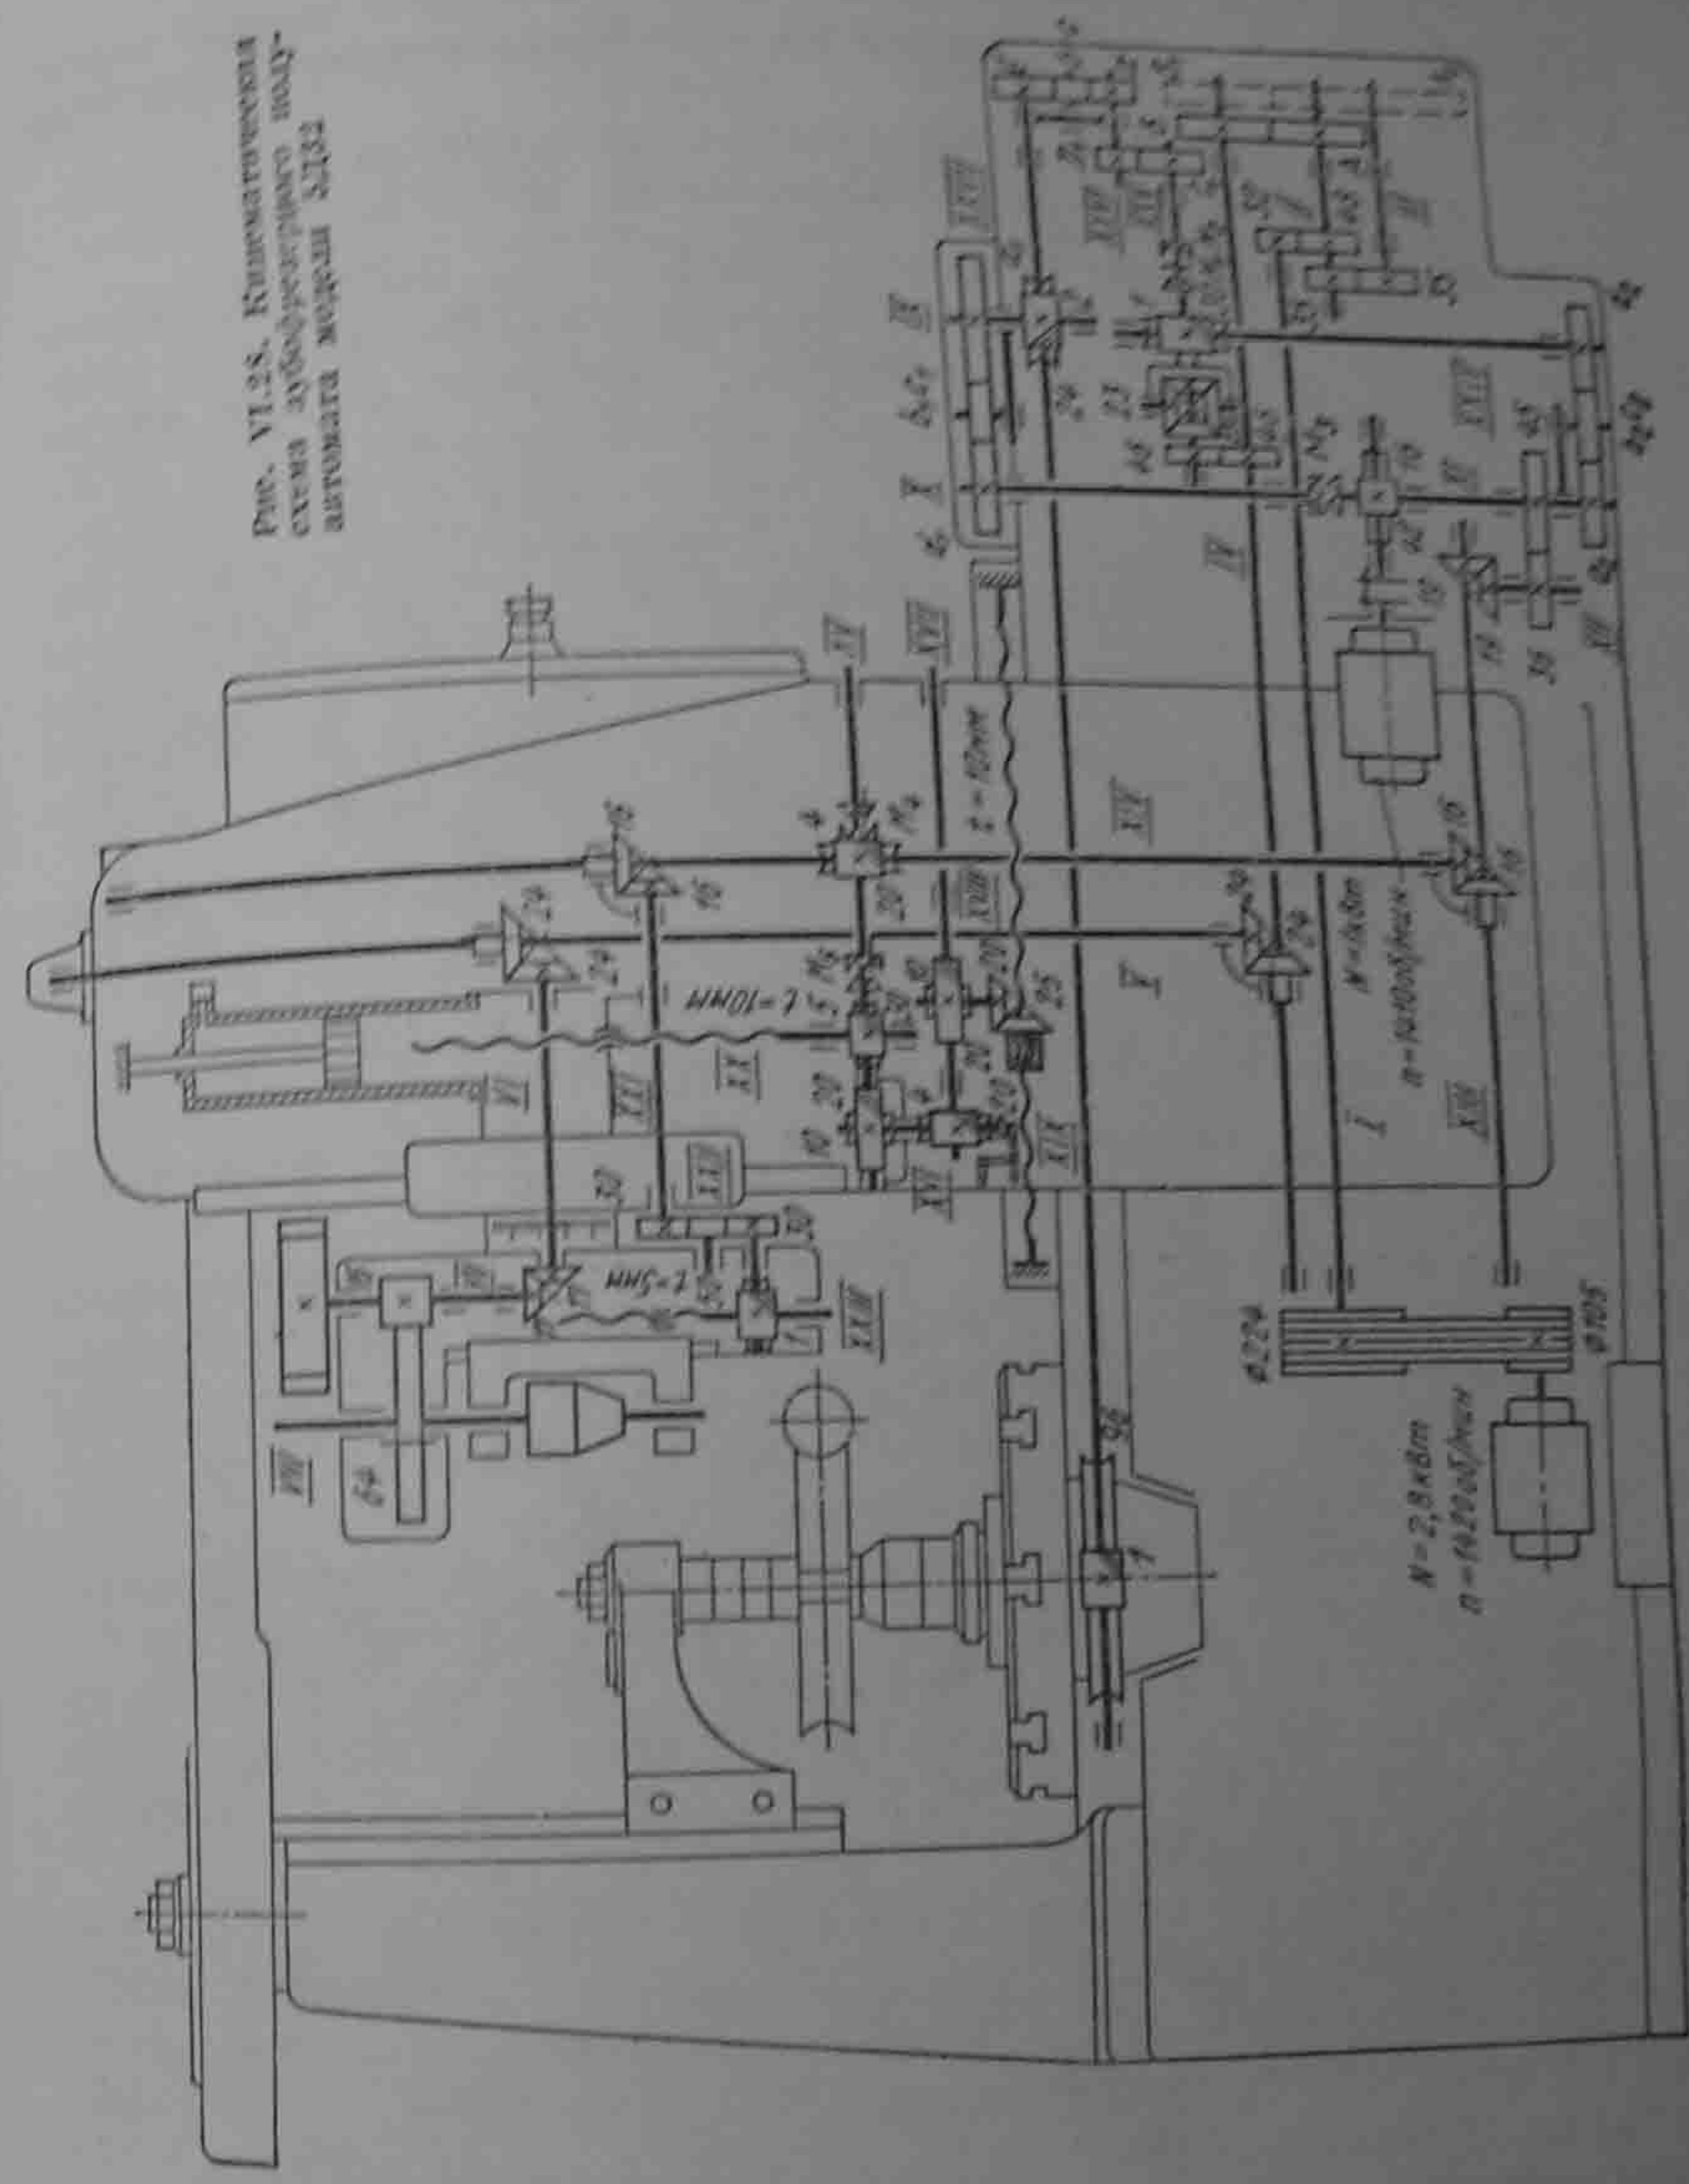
Кинематическая схема зубофрезерного полуавтомата модели 5Д32
